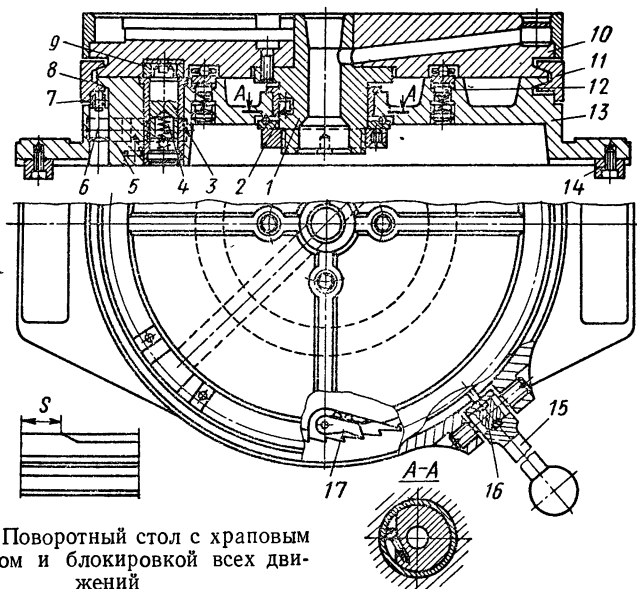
Поворотный стол с храповым механизмом и блокировкой всех движений
